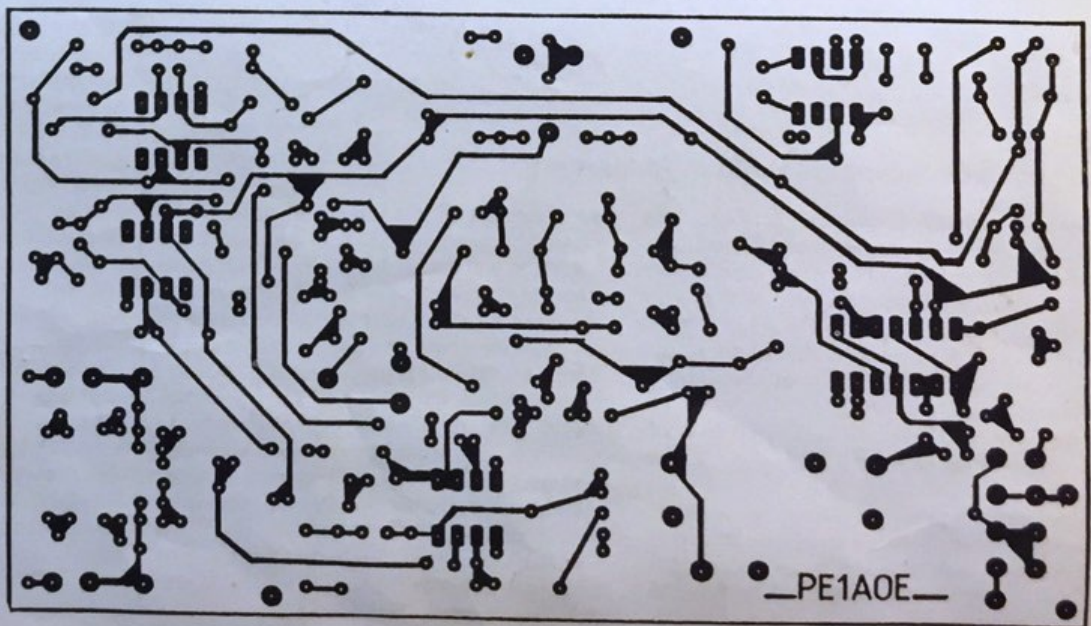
Printlay-out, de componentenzijde is geheel van koper.
